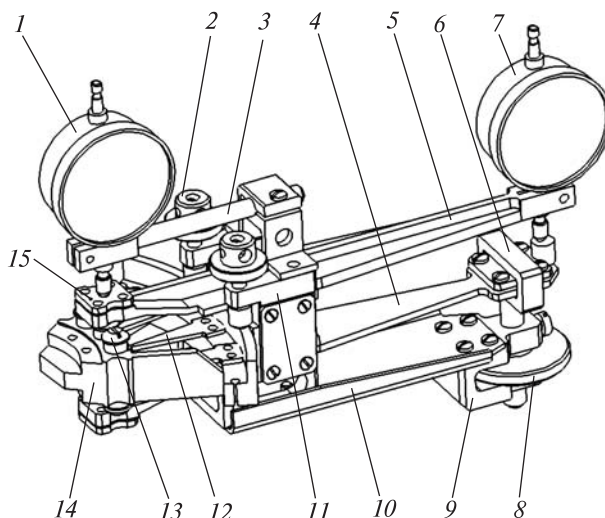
Тарувальний пристрій (1 — індикатор, 2 — притисний гвинт, 3 — кронштейн, 4 — пружний елемент, 5 — важіль, 6 — гвинт, 7 — індикатор, 8 — шків, 9 — гвинтовий механізм, 10, 11 — корпусні деталі, 12 — зразок, 13 — повзун, 14 — касета, 15 — кульова опора)
